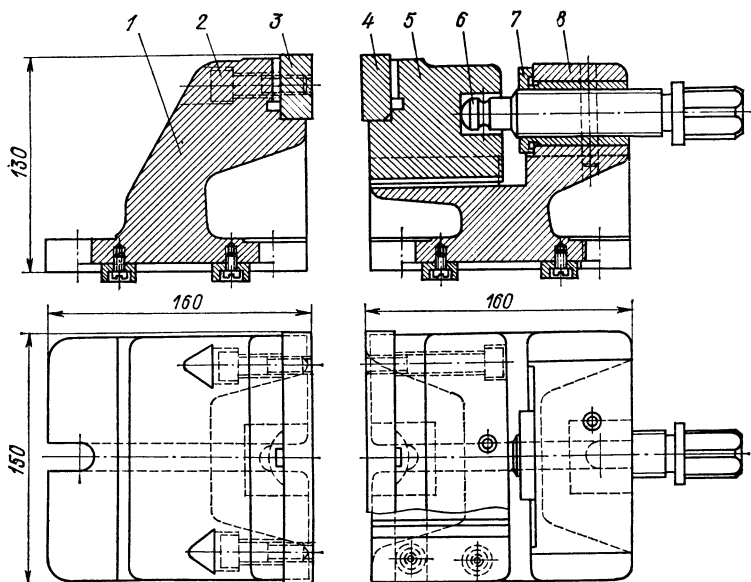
Составные машинные тиски для обработки крупногабаритных деталей
